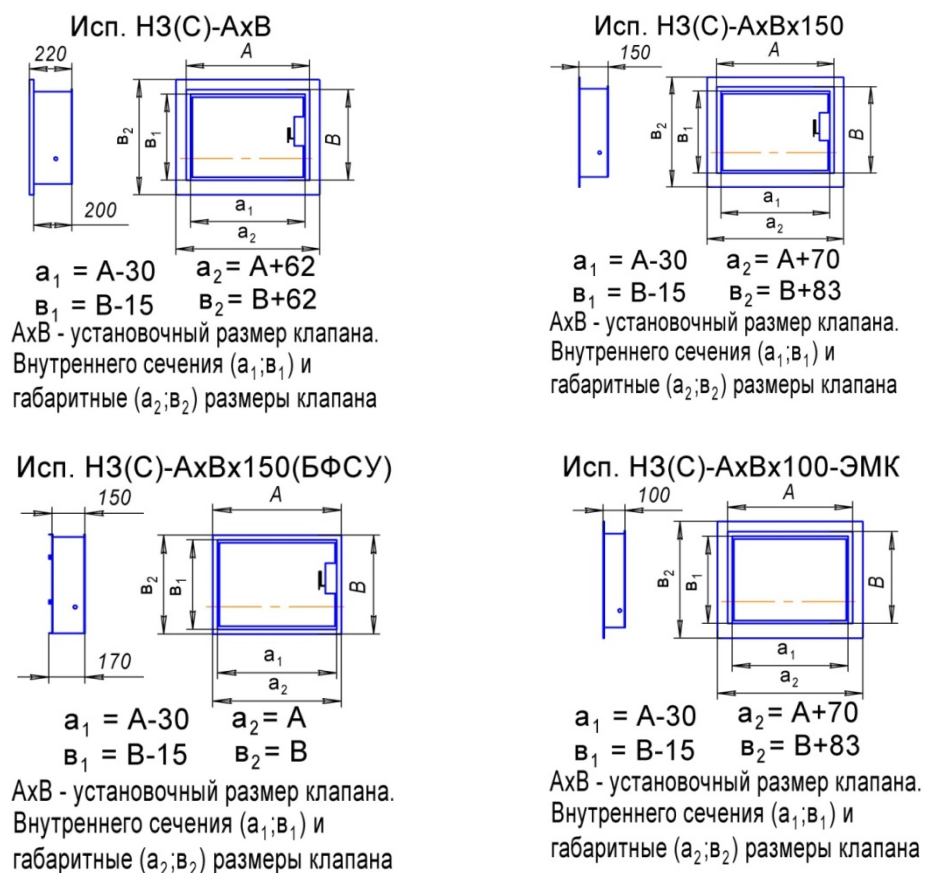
Установочные, габаритные и размеры внутреннего сечения клапана.
